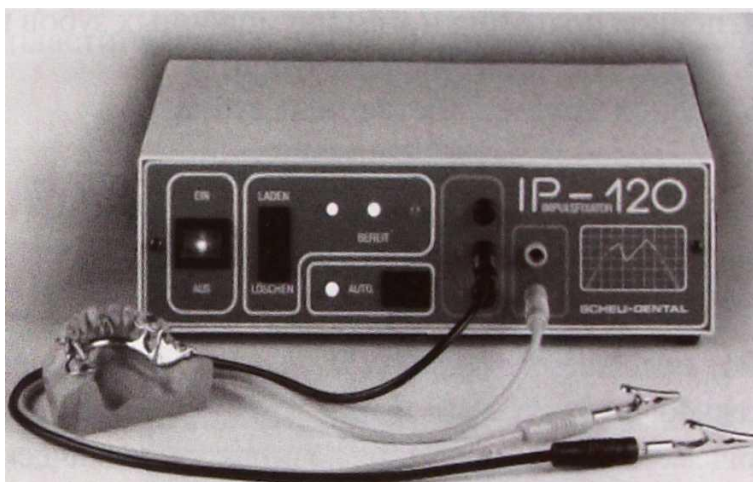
Импульсный сварочный аппарат «IP-120».
